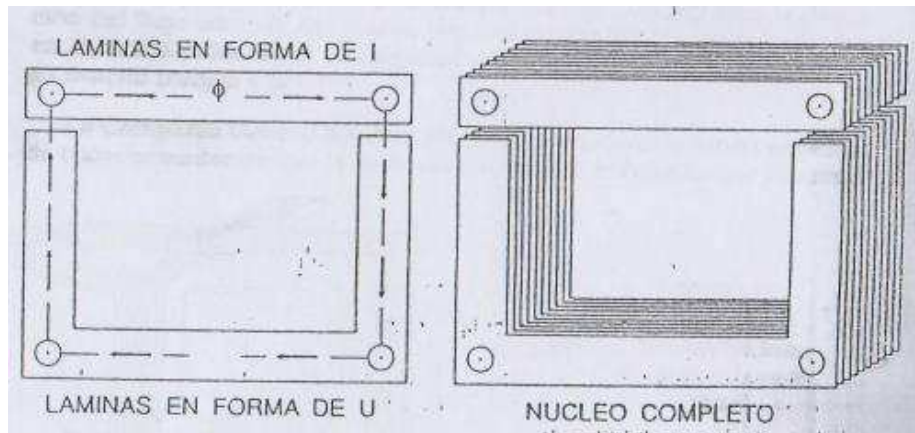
Laminas y núcleo del tipo columnas o cerrado.
